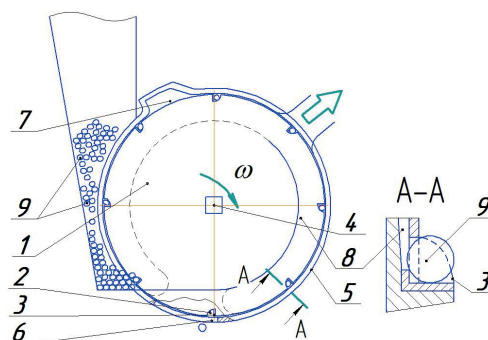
Схема запропонованого пневмомеханічного висівного апарата: 1 – висівний диск; 2 – комірка; 3 – лопатка; 4 – приводний вал; 5 – корпус; 6 – висівне вікно; 7 – пасивний пристрій для видалення зайвого насіння; 8 – вакуумна камера; 9 – насіння
